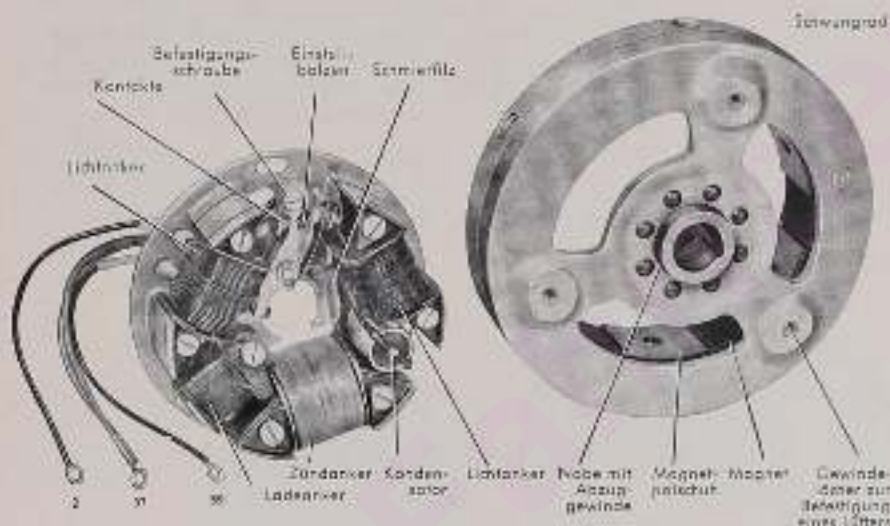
Bosch-Schwunglichtmagnetzylinder LM/UT 1/154/45
